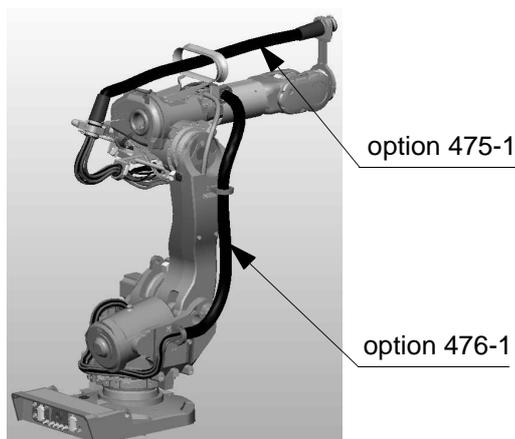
Soudage par points, de la base à l'axe 3 et de l'axe 3 à l'axe 6.
